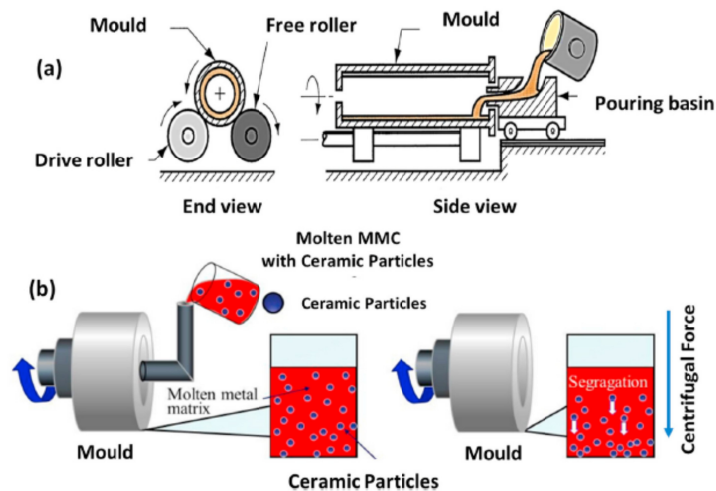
(a) Machine horizontale de coulée centrifuge [El-Galy Islam M., et al. 2019].
